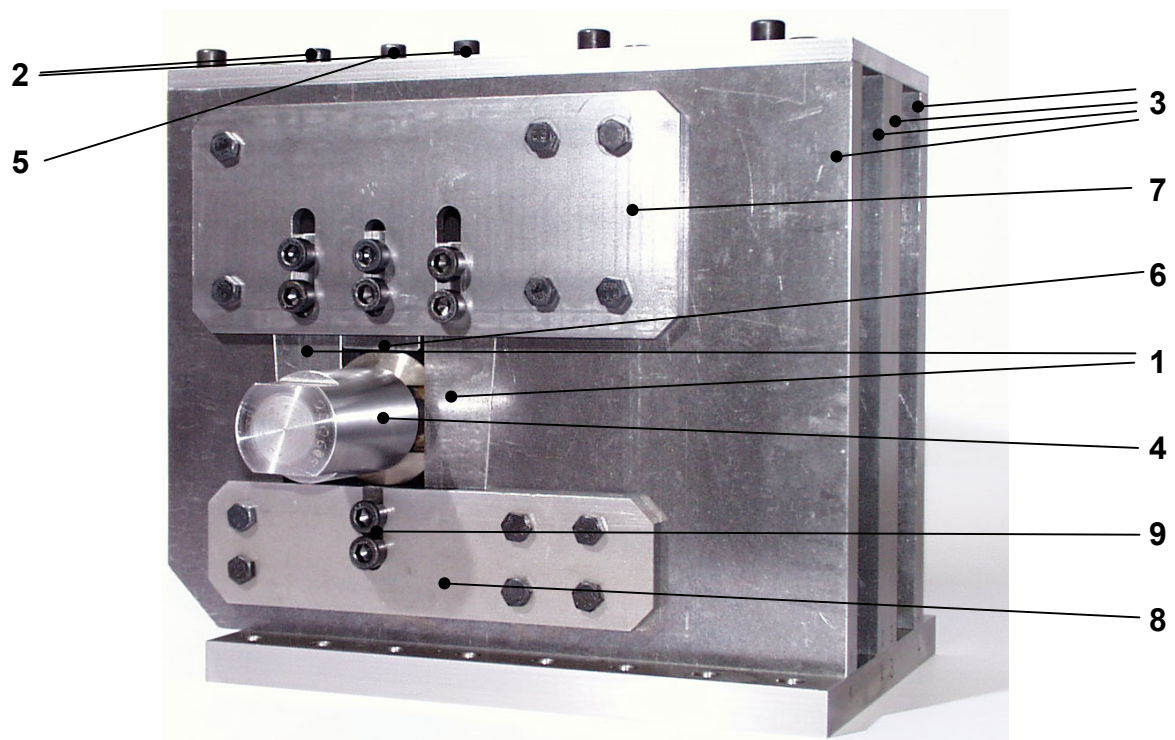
Seitenansicht des Probenhalters für verschiedenartige Momentenableitungen
